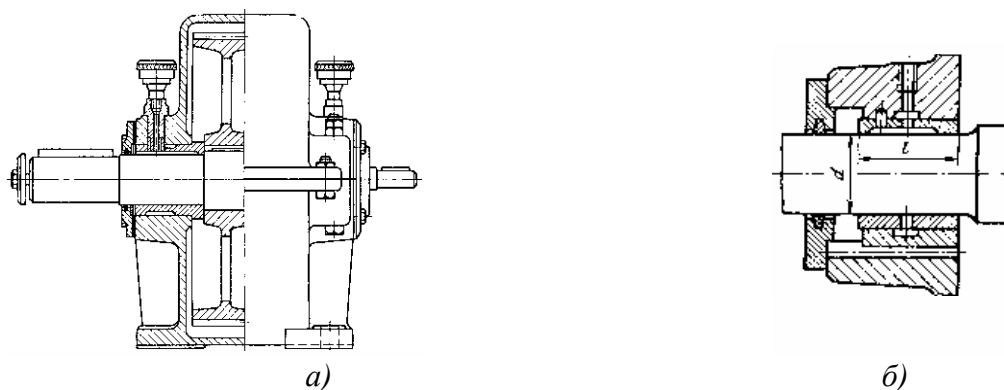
Встроенный подшипник скольжения вала зубчатого редуктора:
